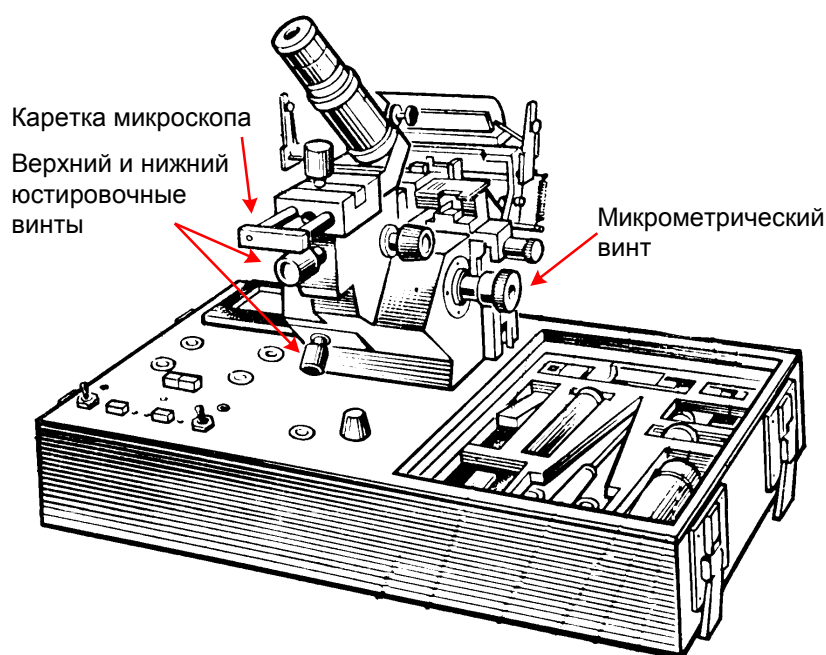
Ручки юстировки сварочного аппарата КСС-111
